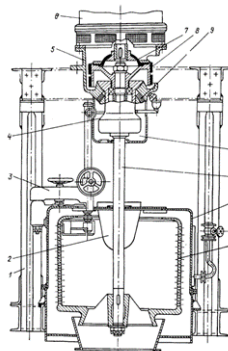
Центрифуга ФПД: 1 - металоконструкція; 2 - лоток;
